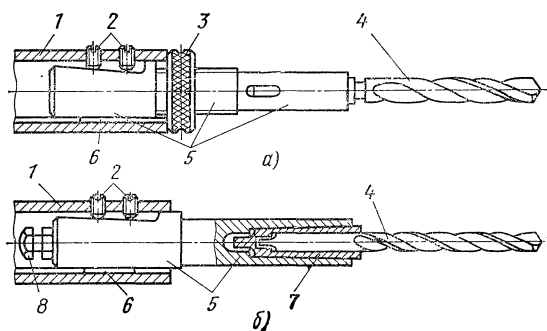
Крепление сверл на агрегатных головках с регулировкой длины гайкой (а) и болтом (б)
